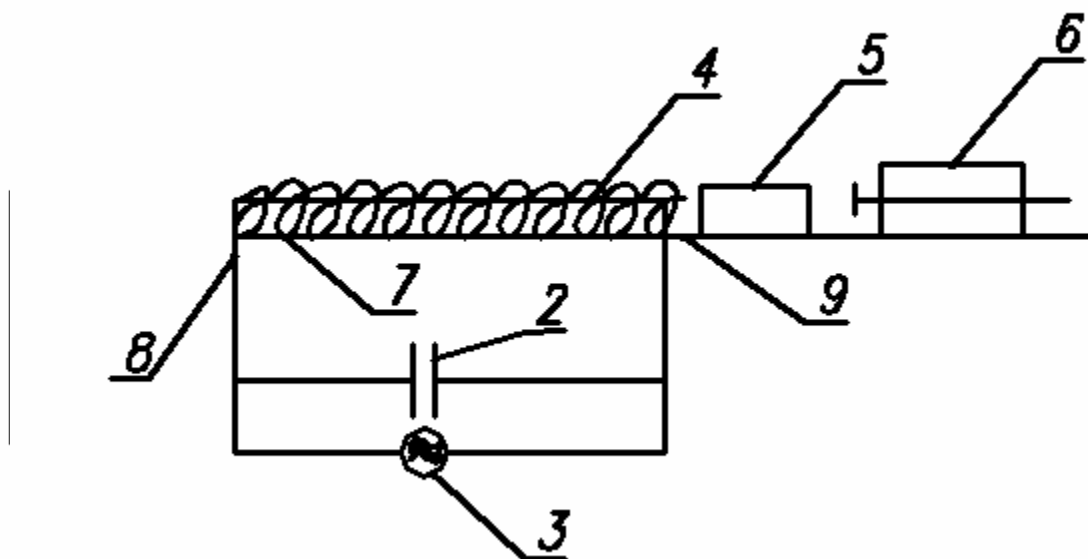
Принципиальная схема индукционной установки: 1 – индуктор; 2 – конденсаторная батарея; 3 – преобразователь тока повышенной частоты в ток высокой частоты; 4 – нагреваемые заготовки; 5 – подающиеся заготовки; 6 – толкатель; 7 – направляющие заготовок
